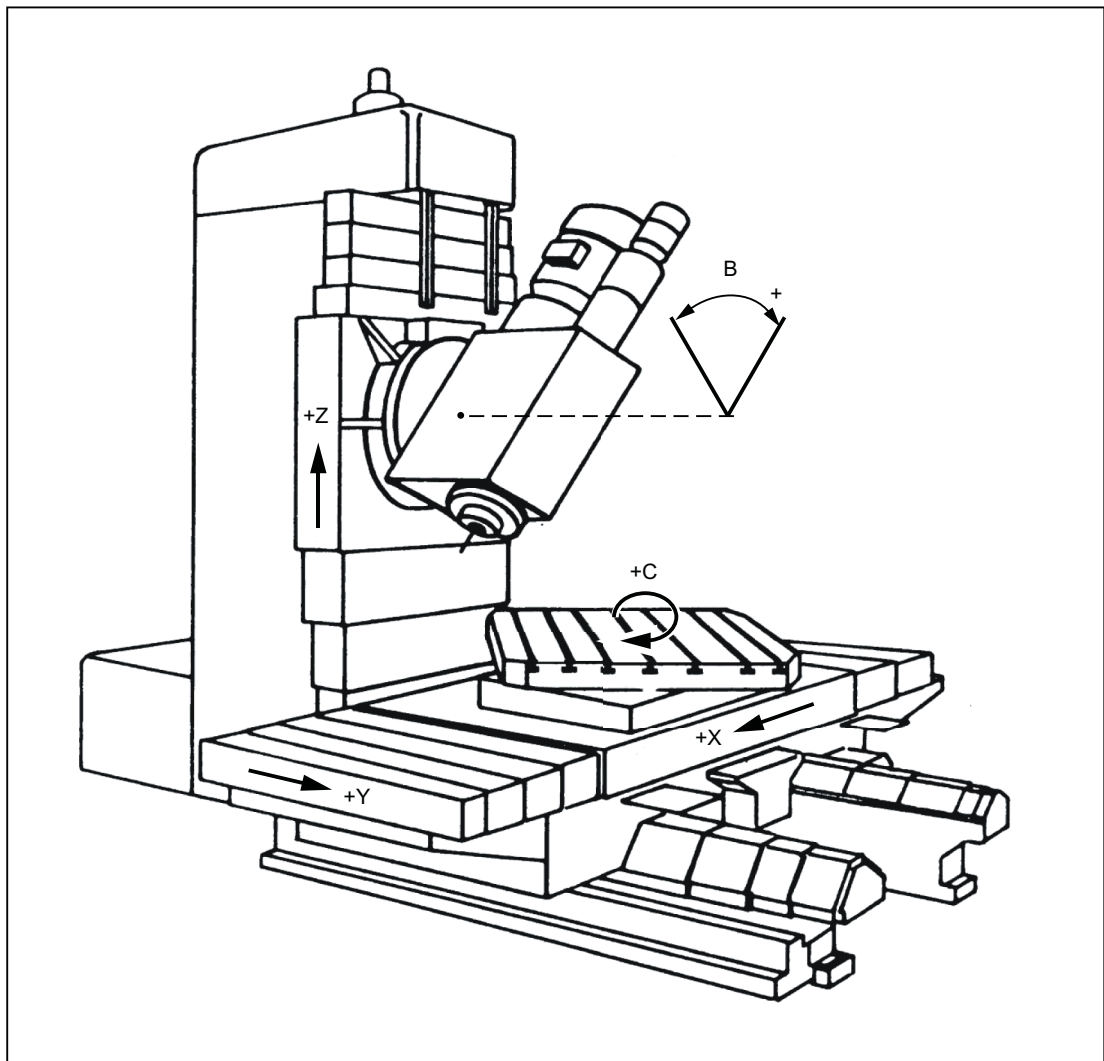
MKS mit den Maschinenachsen X, Y, Z, B, C (5-Achs-Fräsmaschine)
